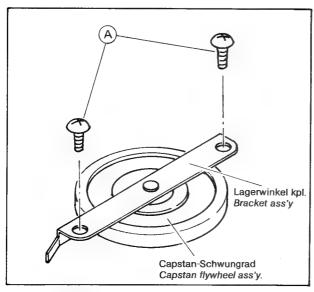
Capstan-Schwungradausbau Fig. 2-13 Capstan flywheel replacement
